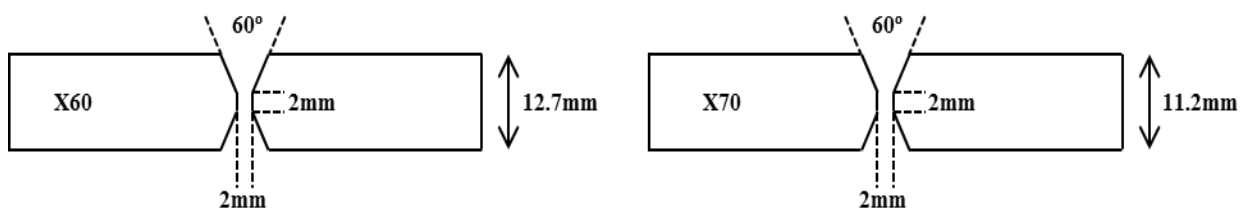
Preparación de las placas de los acero X-60 y X-70 para su soldadura.
